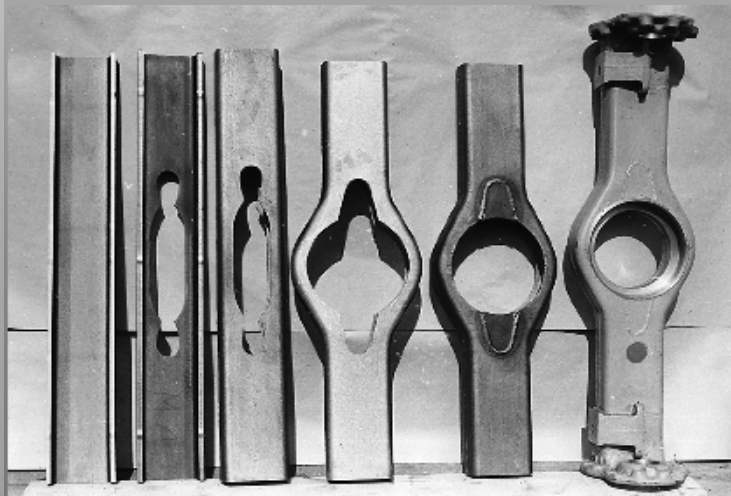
zeigt nochmals die Arbeitsfolge. Nach dem Schweißen der Zwickel wurde der Mittelbereich bearbeitet mit anschließendem Einschweißen des Mittelrings. Es erfolgte das Ablängen des Achsrohres und Anschweißen der Tragflansche. Komplettiert wurde der Achskörper mit den Federauflagen. Die Betriebsmittel waren jeweils mechanisiert.
